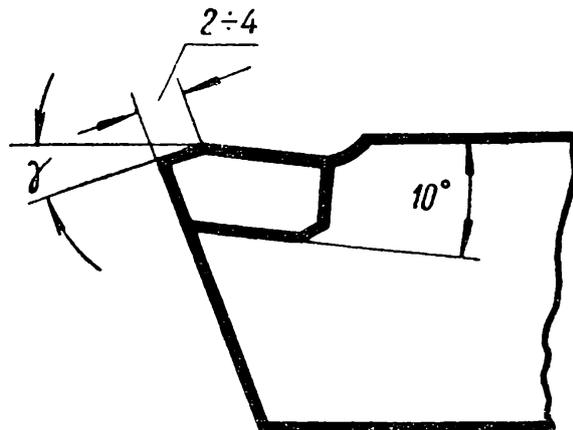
б. Плоская заточка передней поверхности резца (пластинки твердого сплава) с отрицательным передним углом.
